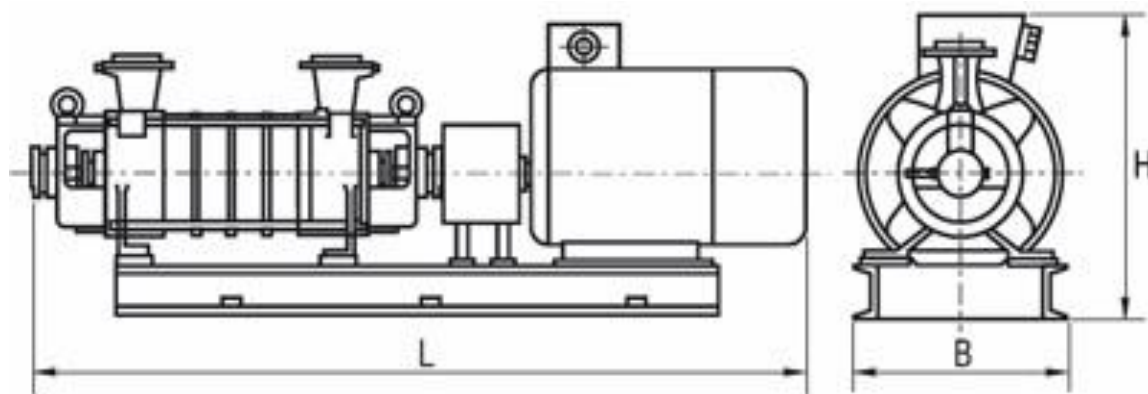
Габаритный чертёж насоса ЦНСГ-300-240
